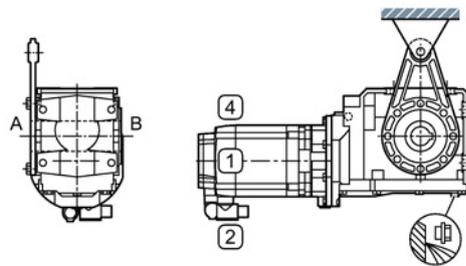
Einbaulagen für Kegelradgetriebe B.Z (Flansch-) oder B.Z (Gehäuseflanschausführung), Baugröße 39 - 49, 2-stufig
